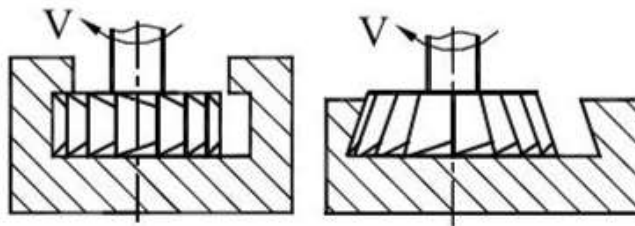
Схеми фрезерування пазів закритого профілю.
